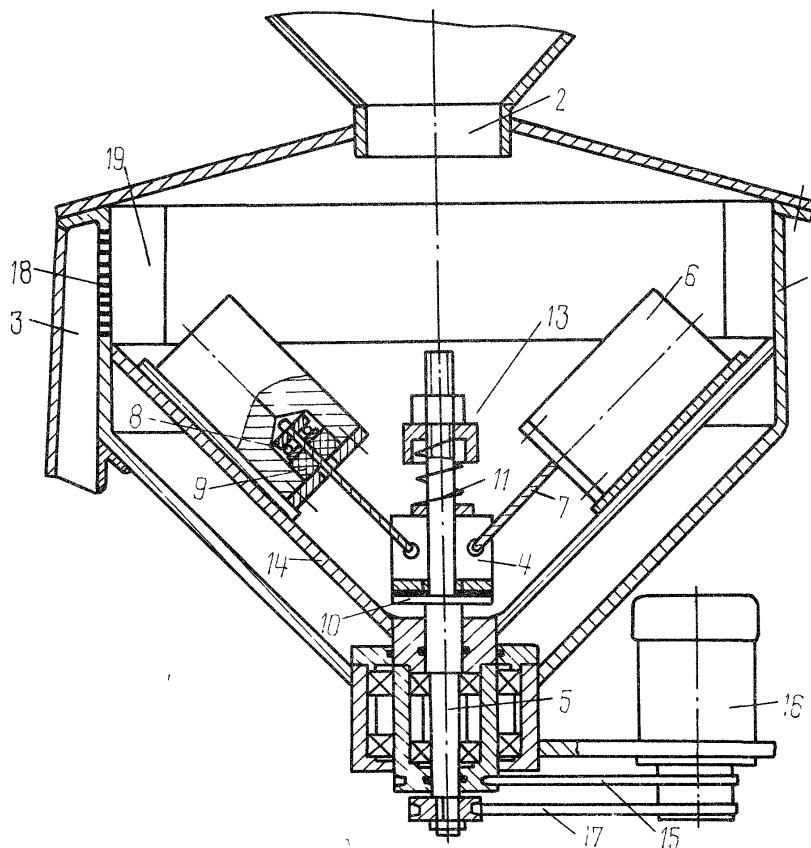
Загальний вигляд інерційного млина з конічною чашею
